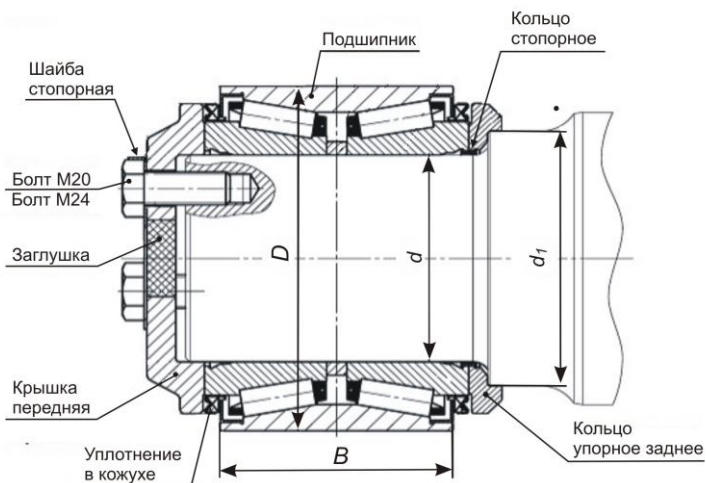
Конический подшипниковый узел под адаптер с базовым подшипником в габаритных размерах 150×250×160 мм марки «Timken»
